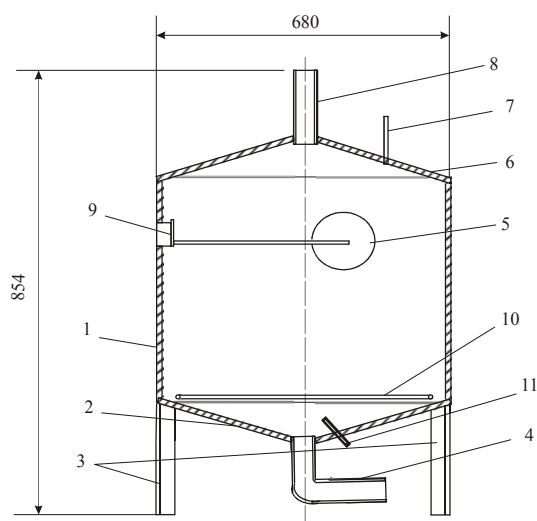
Приёмно-заборное устройство битума «погружного» типа. 1 – цилиндрический корпус, 2 – дно, 3 – ножки, 4 – заборный патрубок, 5 – поплавок, 6 – крышка, 7 – воздушный клапан, 8 – приёмный патрубок, 9 – входной патрубок, 10 – теплоэлектрический нагреватель (ТЭН), 11 – датчик температуры
